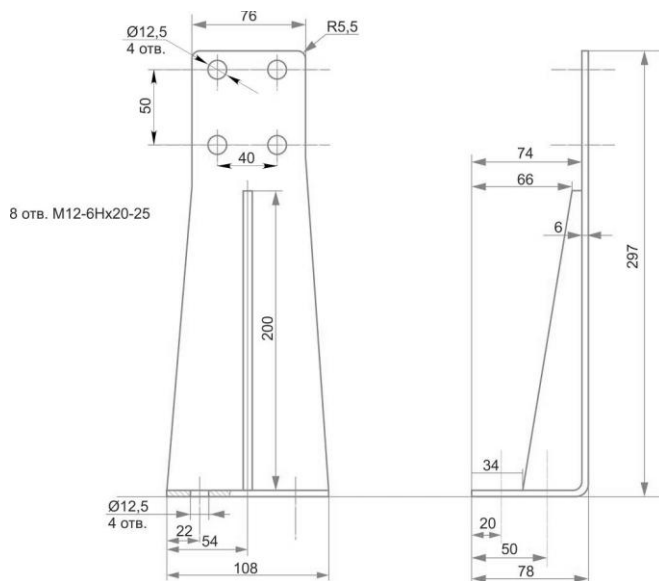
Загальний вид складального креслення задніх опір двигуна
